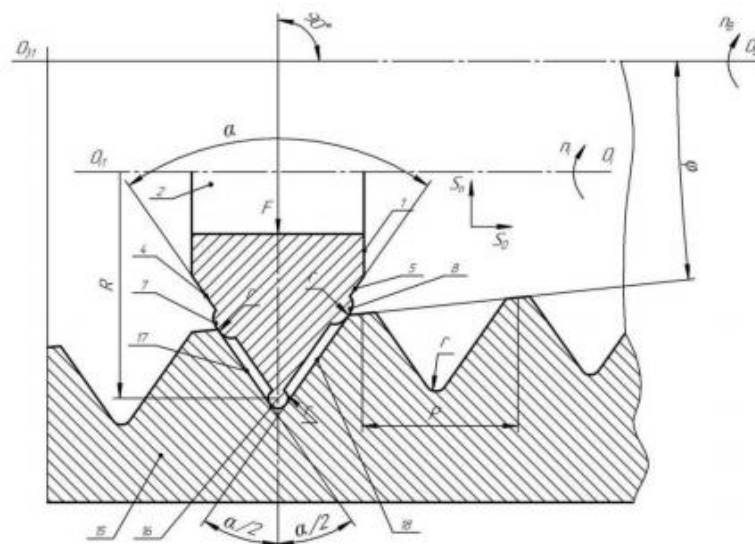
Схема фрикційного зміцнення різьбової поверхні [27]
